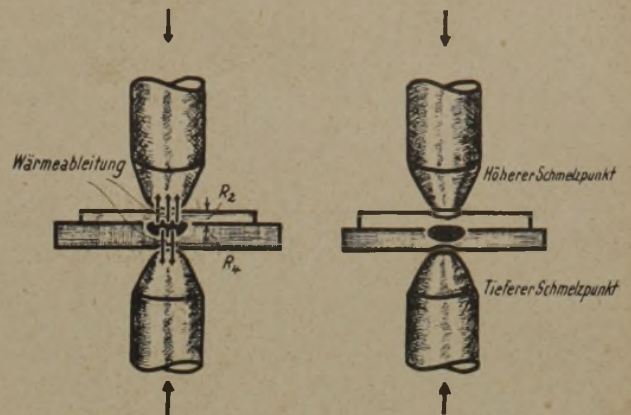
Elektrische Punktschweißung, Unsymmetrie der Schweißlinse
